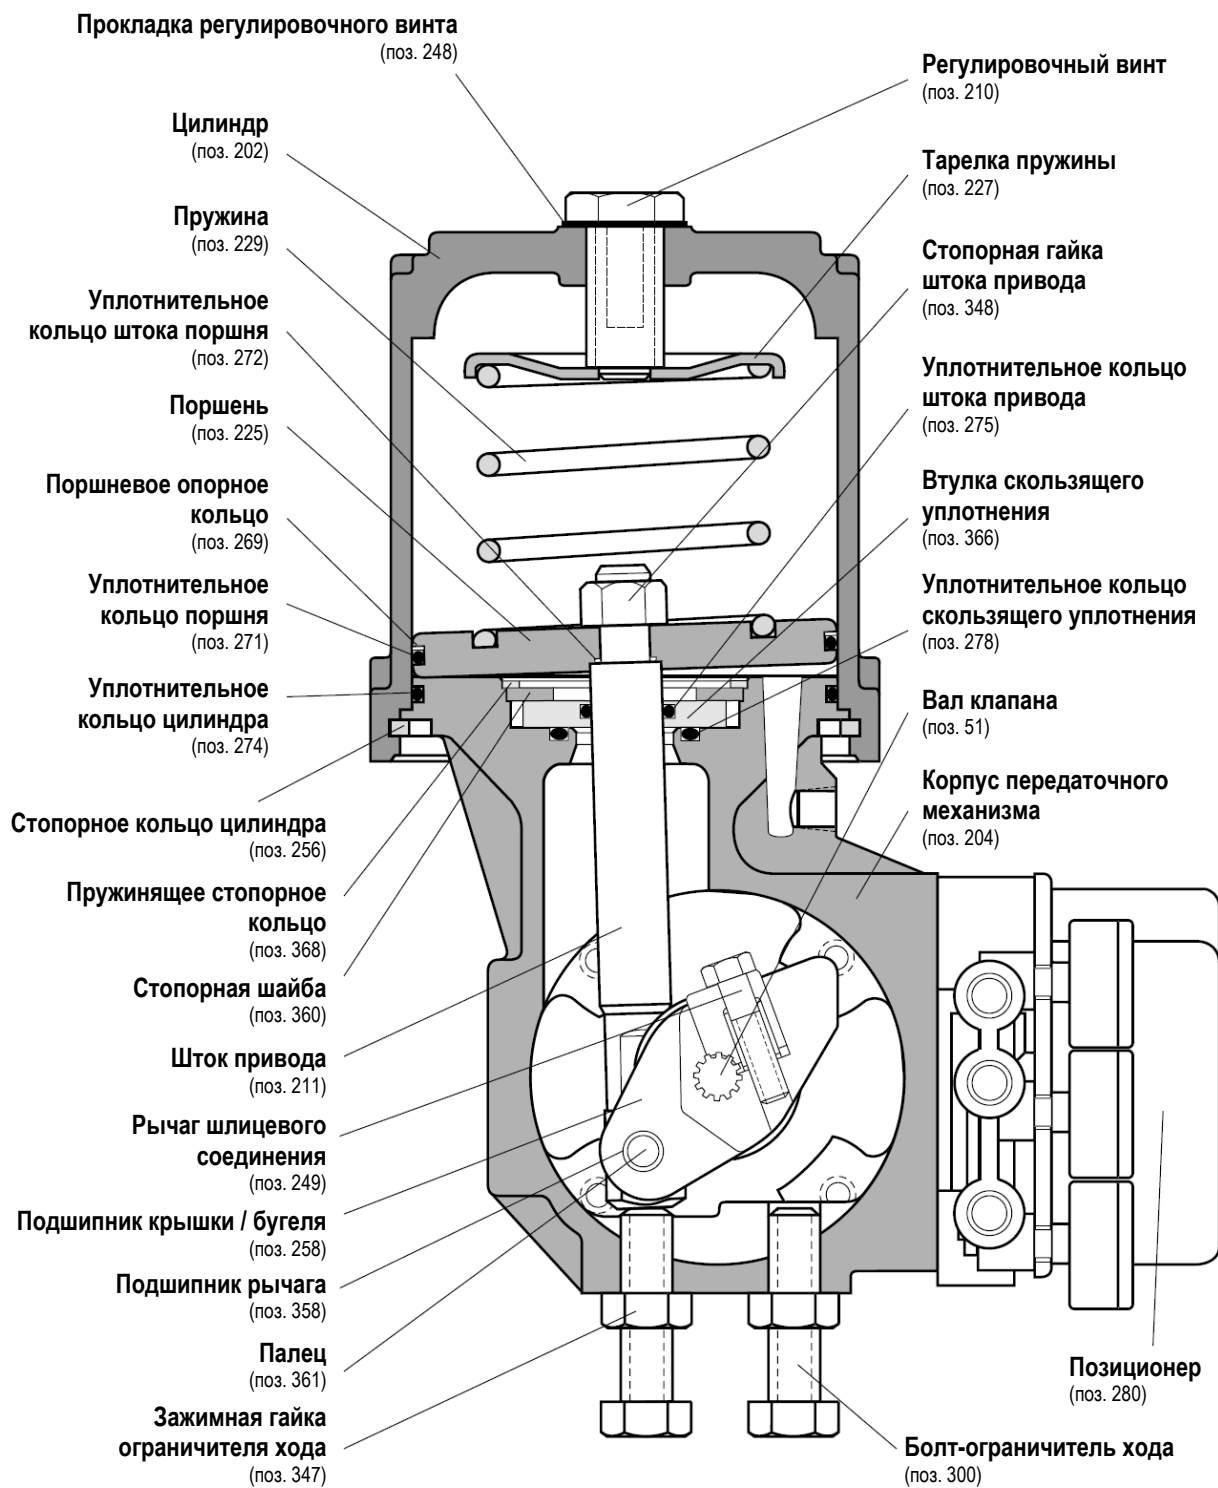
Привод с рычагом без зажима. Вид в разрезе
